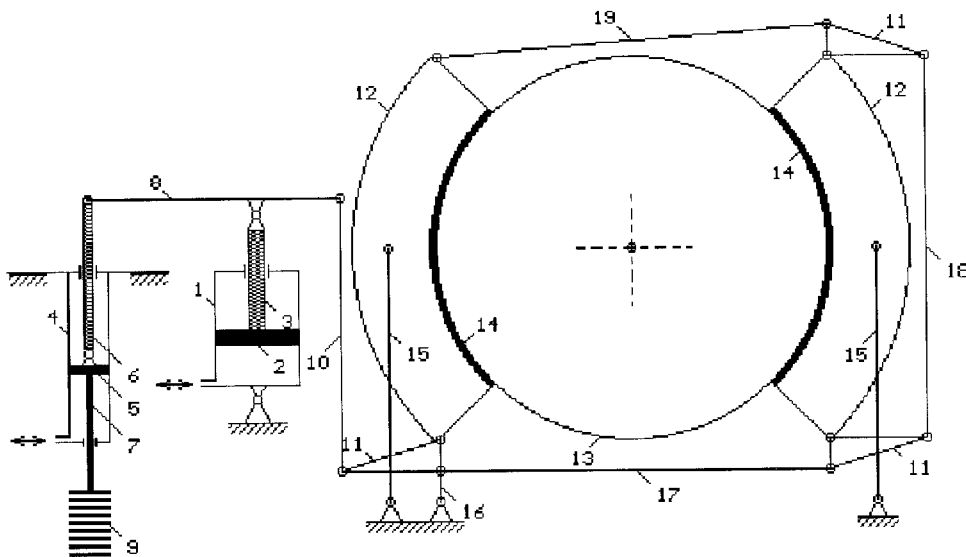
Схема вантажно-пневматичного приводу гальма
